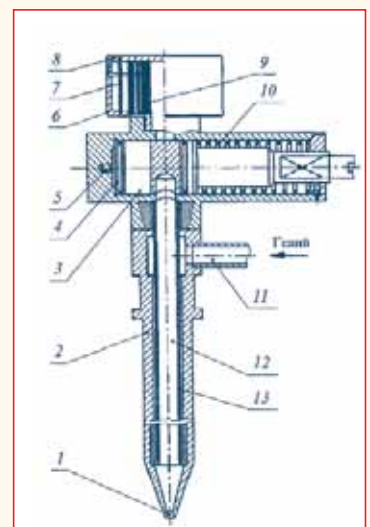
Схема отборника: 1 - приёмное отверстие, 2 - корпус, 3 - канал, 4 - затвор, 5 - трубка подачи воздуха, 6 - ловушка конденсата, 7 - пористый фильтр, 8 - дроссель, 9 - лабиринт, 10 - пружина, 11 - трубка подвода гелия, 12 - газоход, 13 - рубашка охлаждения
